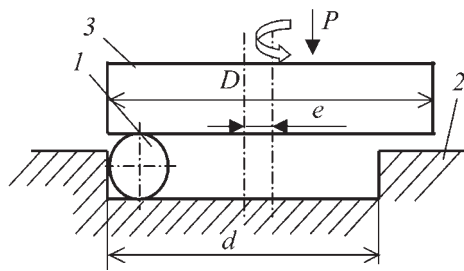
Схема накатывания сферической заготовки плоскими поверхностями
